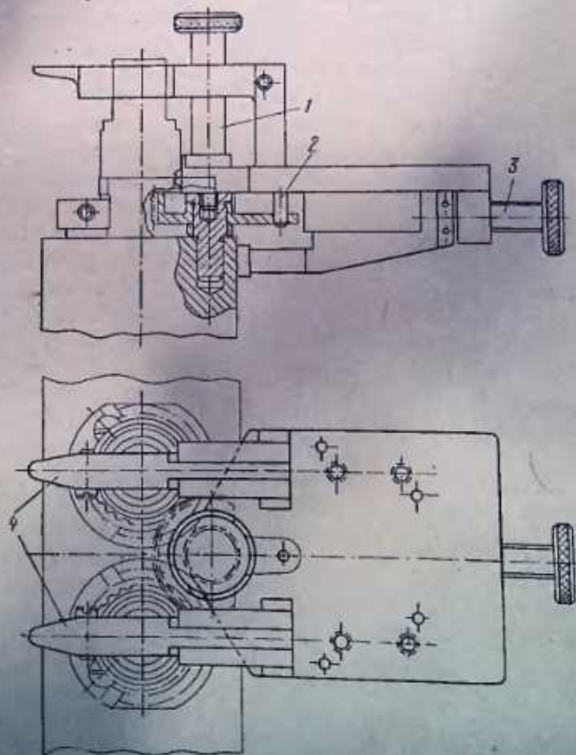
Приспособление ЛМ9579-468 для установки на корпус насоса поворотных втулок 1М.30.07
